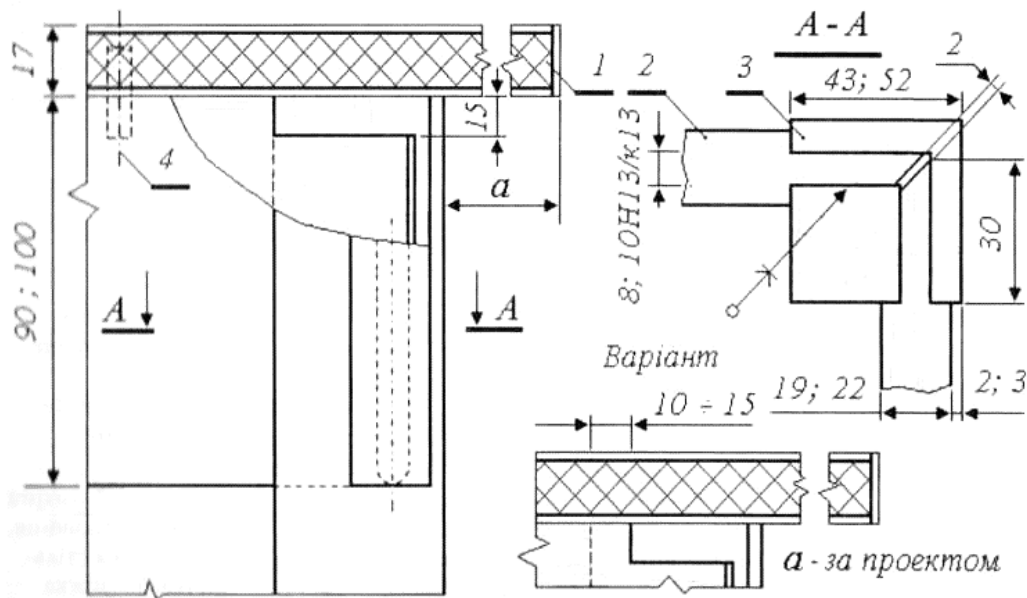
З'єднання ніжок з царгами стола нерозбірного: 1 – стільниця, 2 – царга, 3 – ніжка, 4 – шканти
